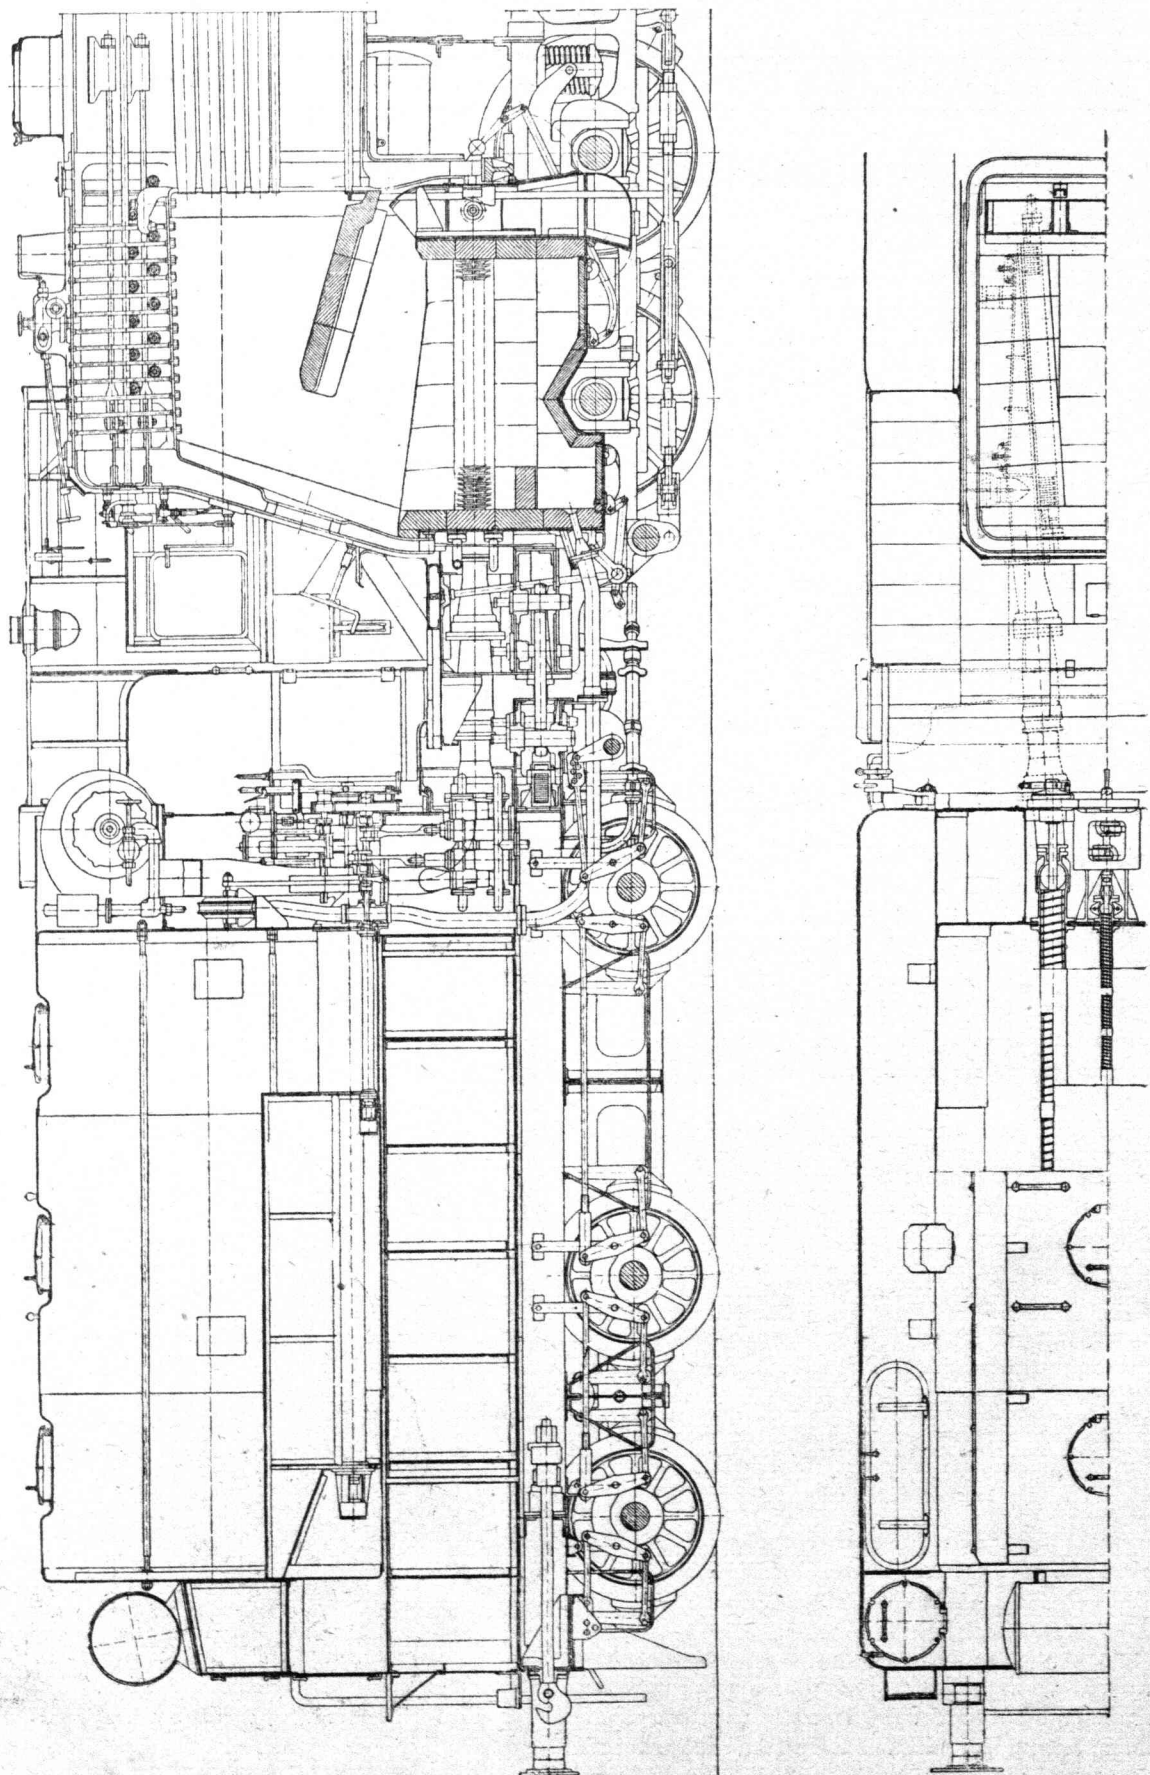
Kohlenstaub-Lokomotive, Längsschnitt und Grundriß.
